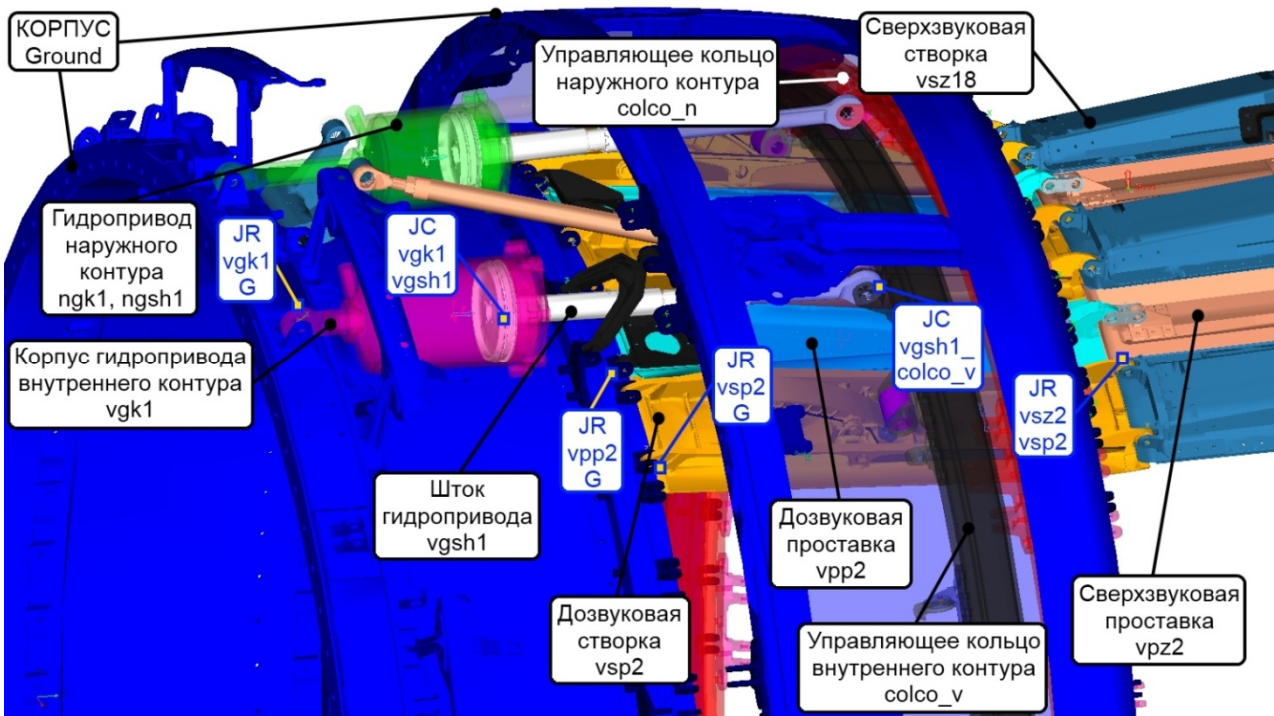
Вид 3D-модели с обозначениями (внутренний контур, зона гидроприводов)
